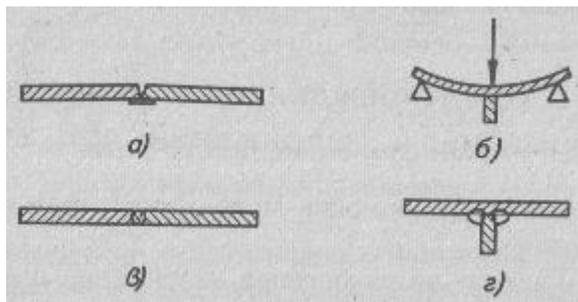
Методы подготовки конструкции к сварке:
